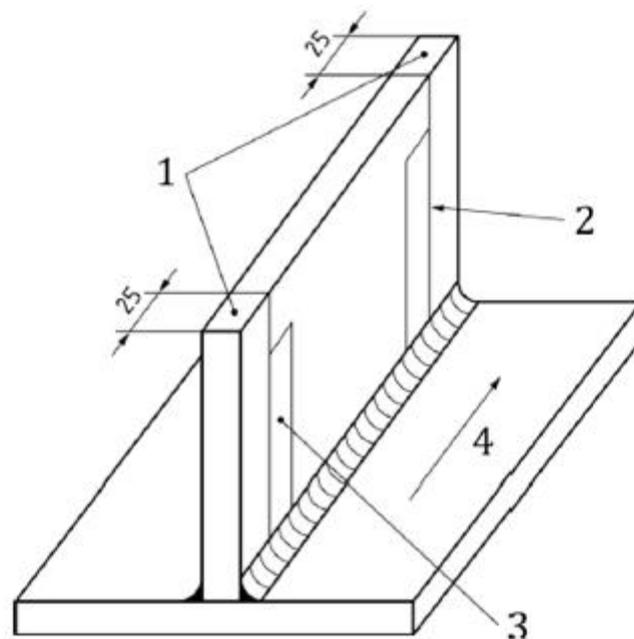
Posiciones de soldadura 2/2. [10]
